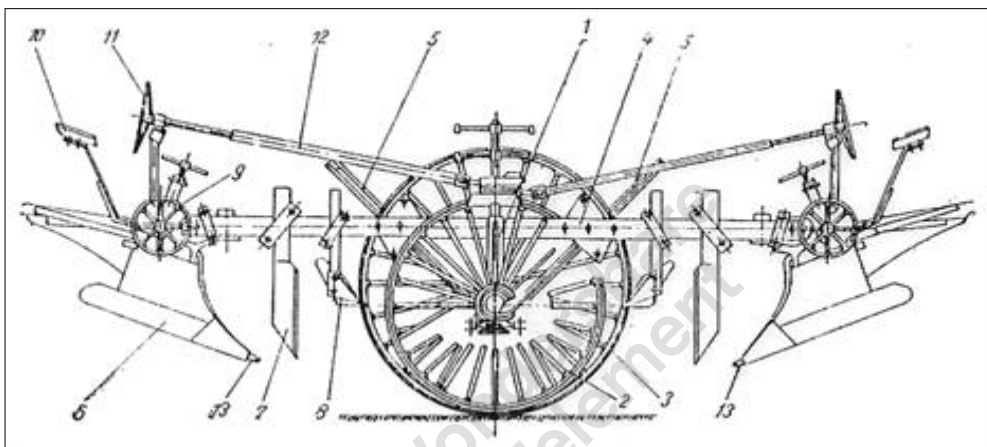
Schema constructivă a plugului balansier pentru desfundat - PBD-60
